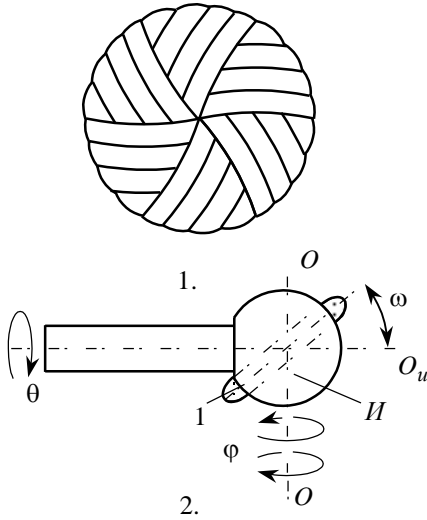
Бор-фреза с групповым расположением зубьев (1) и схема вышлифовывания стружечных канавок (2).
